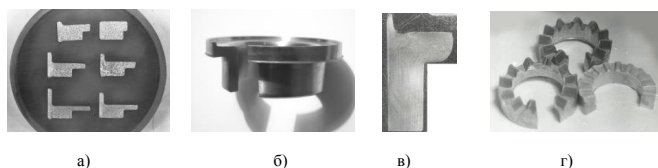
Загальний вигляд і перерізи заготовок, сформованих методами ШО за схемами прямого і зворотного витискування
